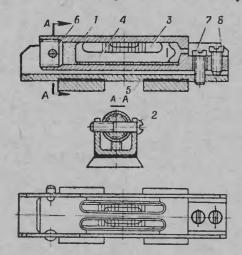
Уровень контрольный УК; 1- трубка: 2- винт; 3- ампула; 4- оправка; 5- корпус; 6- пробка; 7- прижимной винт; 8- упорный винт
